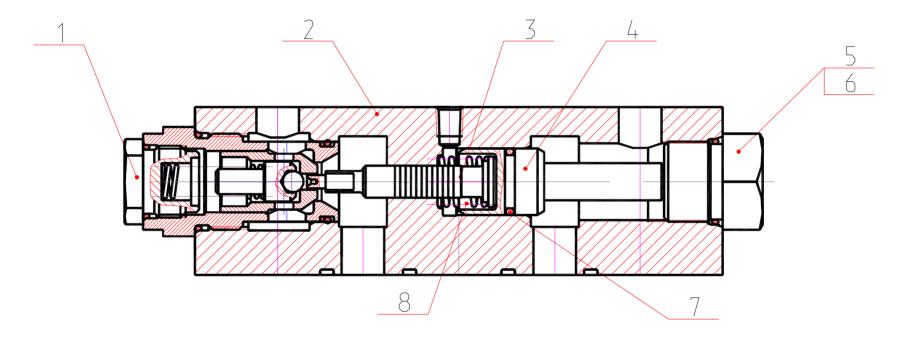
Гидрозамок односторонний Fig. 28 One-Sided Hydraulic Lock
